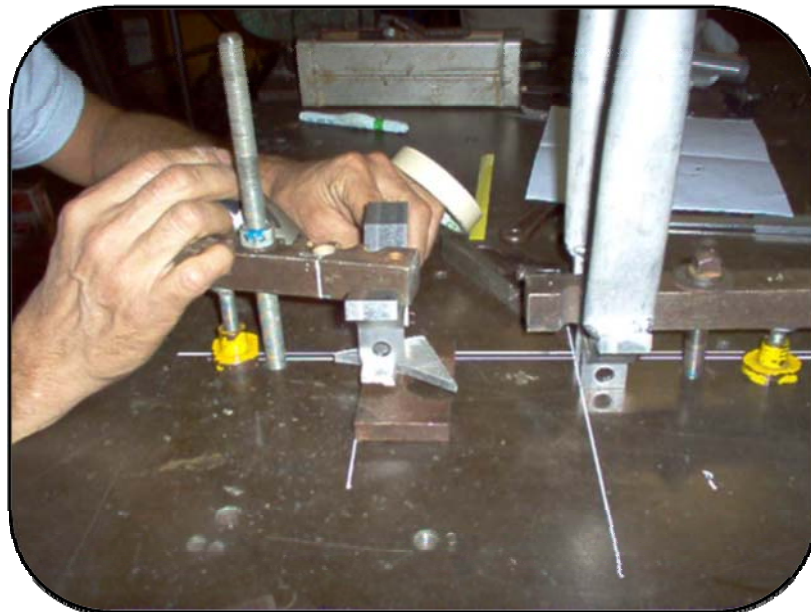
Ensamble y soldadura de la tijera. Segunda etapa
